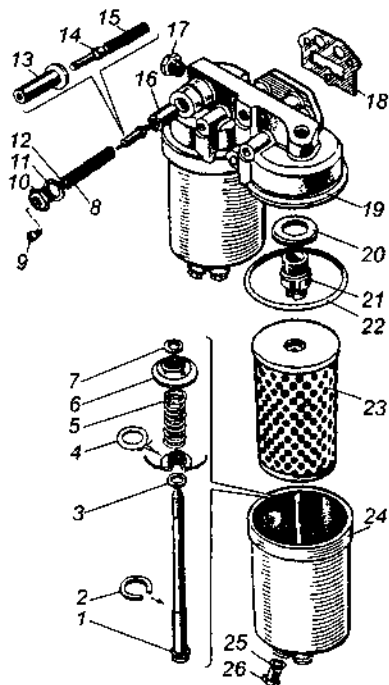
Полнопоточный фильтр для грубой очистки масла: 1 — стержень; 2 — стопорное кольцо; 3 — шайба; 4 — уплотнительное кольцо; 5 — пружина колпака; 6 — уплотнительная чашка; 7 — шайба; 8 — пружина перепускного клапана; 9 — винт сигнализатора; 10 — пробка перепускного клапана; 11, 18, 20, 25 — прокладки; 12 — регулировочная шайба; 13 — корпус сигнализатора; 14 — подвижной контакт сигнализатора; 15 — пружина контакта сигнализатора; 16 — перепускной клапан; 17 — пробка; 19 — корпус фильтра; 21 — втулка корпуса; 22 — уплотнительное кольцо; 23 — фильтрующий элемент; 24 — колпак; 26 — сливная пробка
